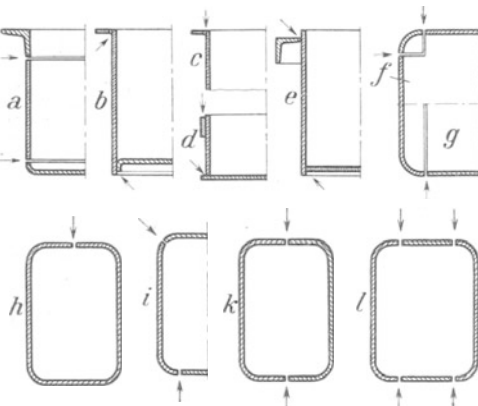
Vorbereitung von Blechkästen zur Schweißung.
